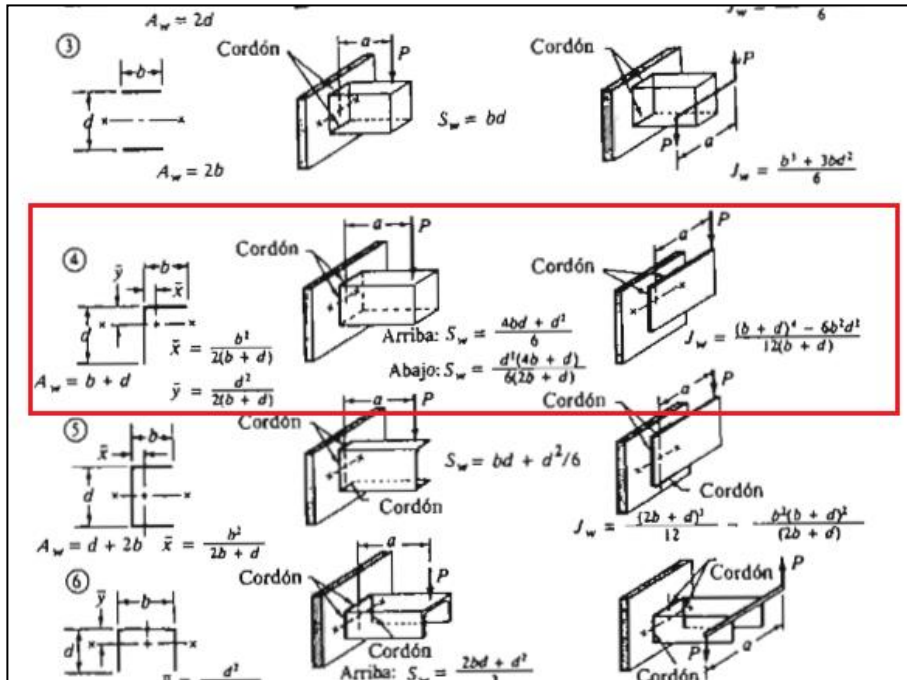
Factores geométricos para el análisis de soldaduras, tomada de «Diseño de elementos de máquinas» por Mott. 2006. p. 786
